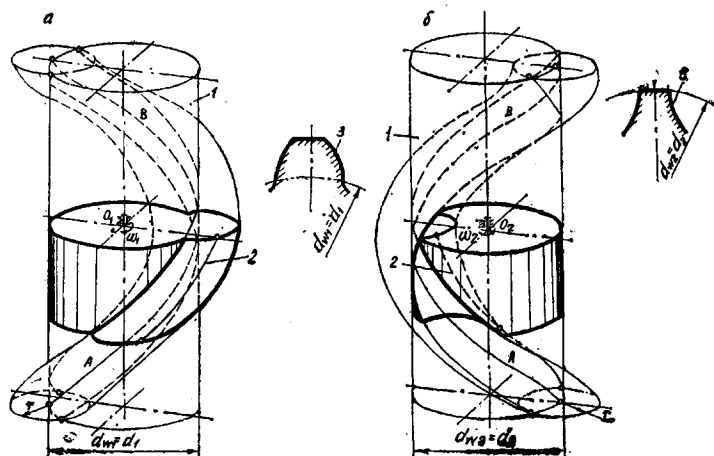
Образование поверхности зуба шестерни (а) и колеса (б) заплуюсного зацепления:
